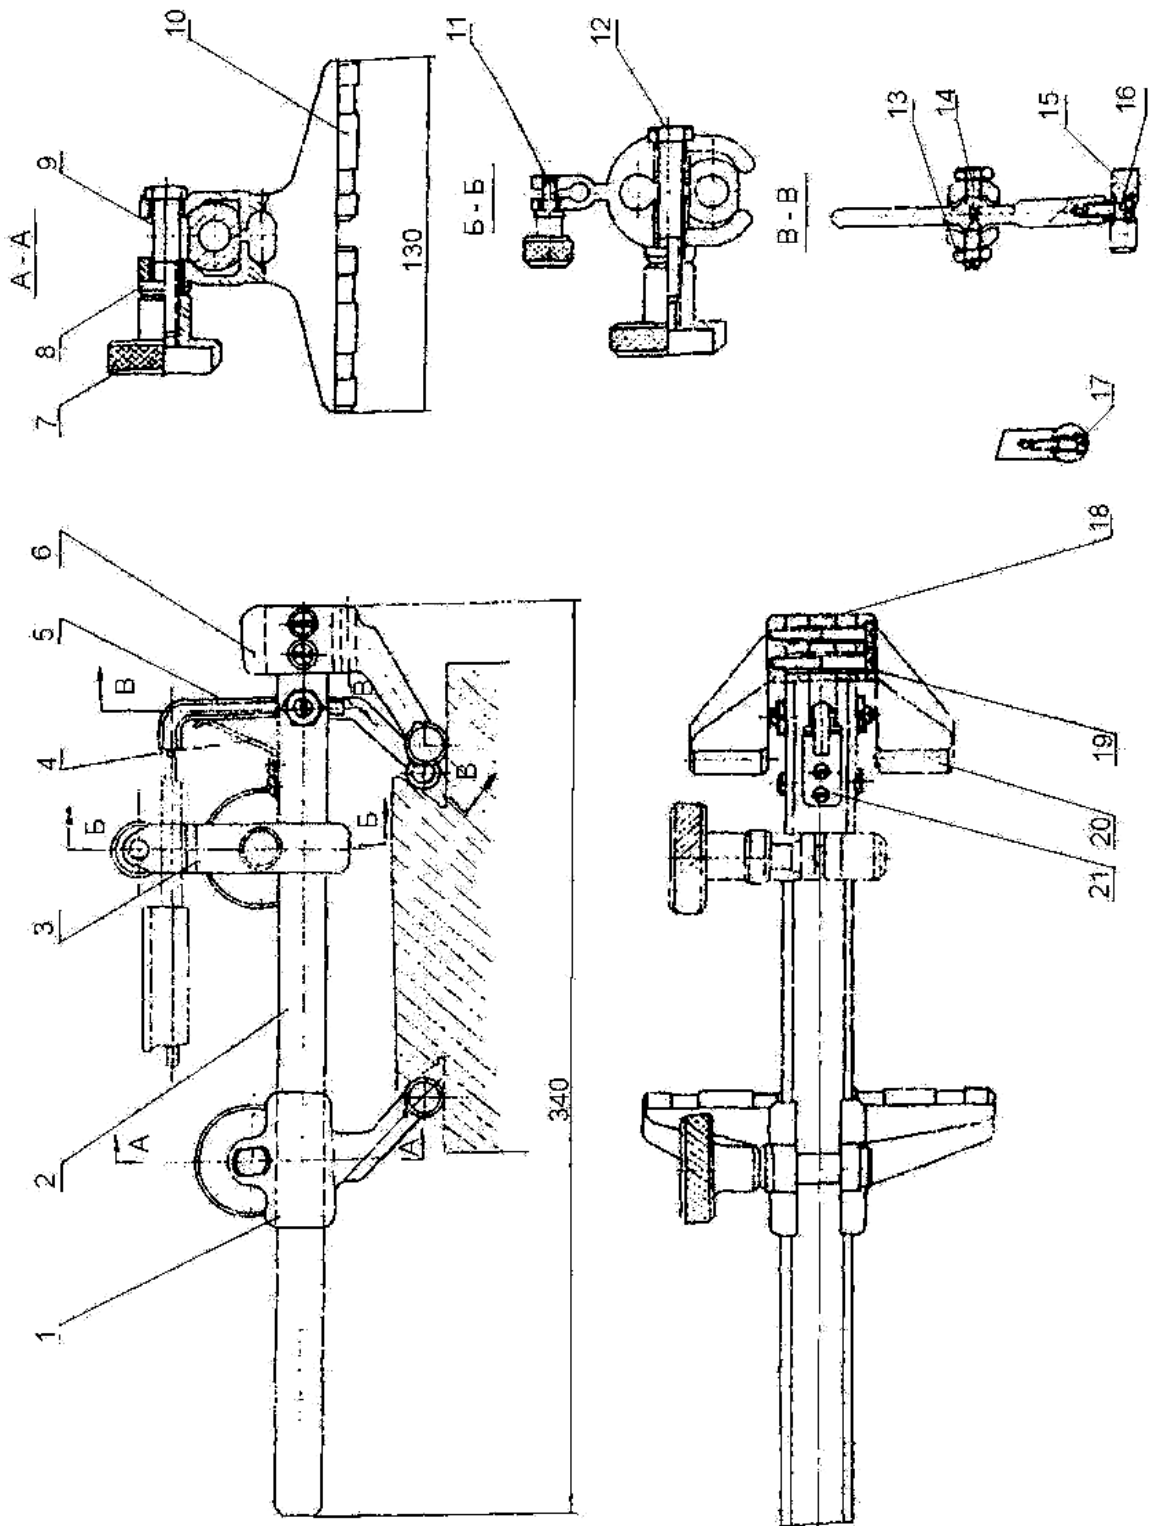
Приспособление для проверки направляющих типа «ласточкин хвост» СД 8532 – 4011
